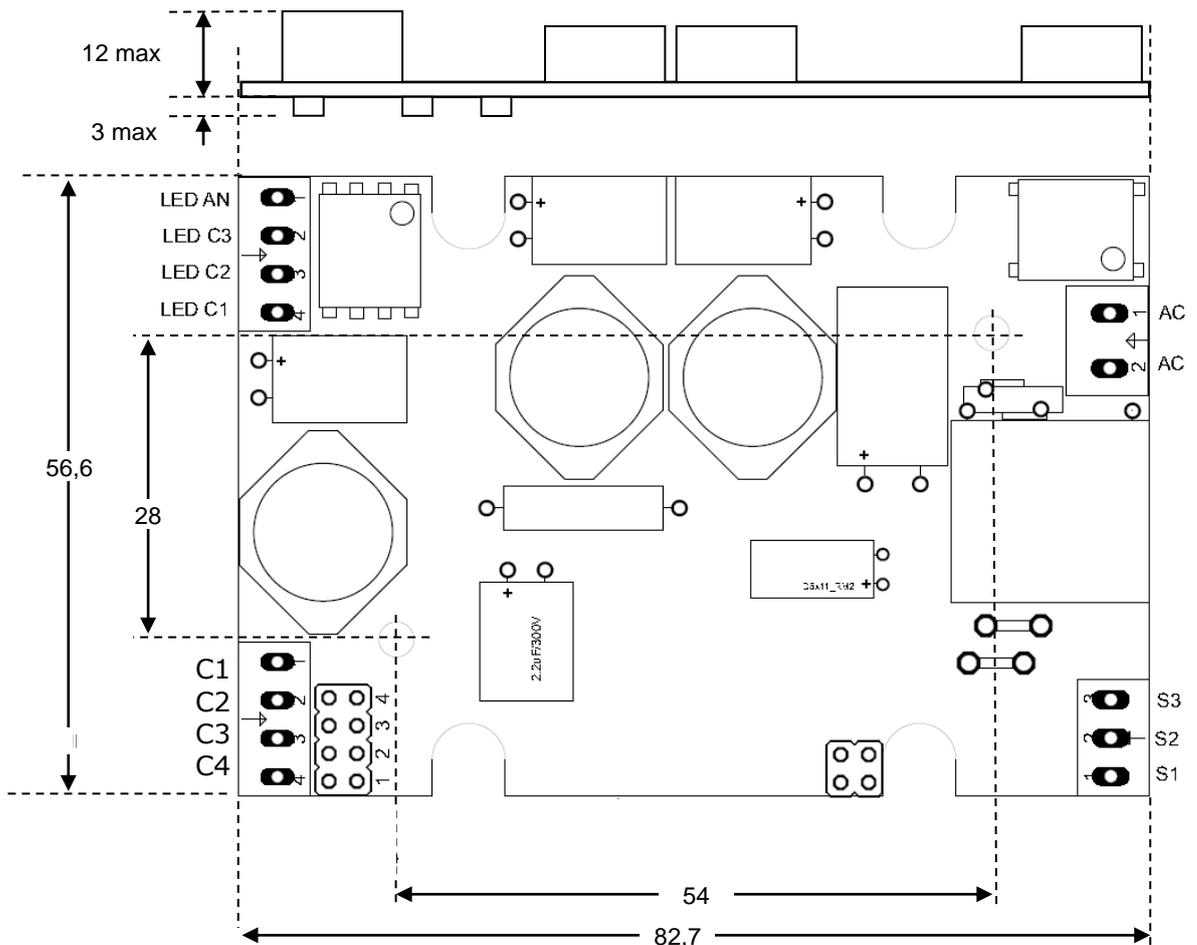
Dimmer, Board-Version (Befestigungsbohrungen Ø 3,2mm (2x), Masse in mm)
